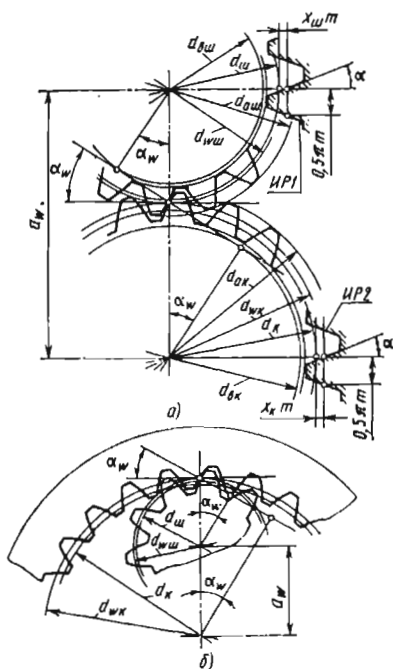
Элементы зацепления цилиндрических зубчатых колес:
